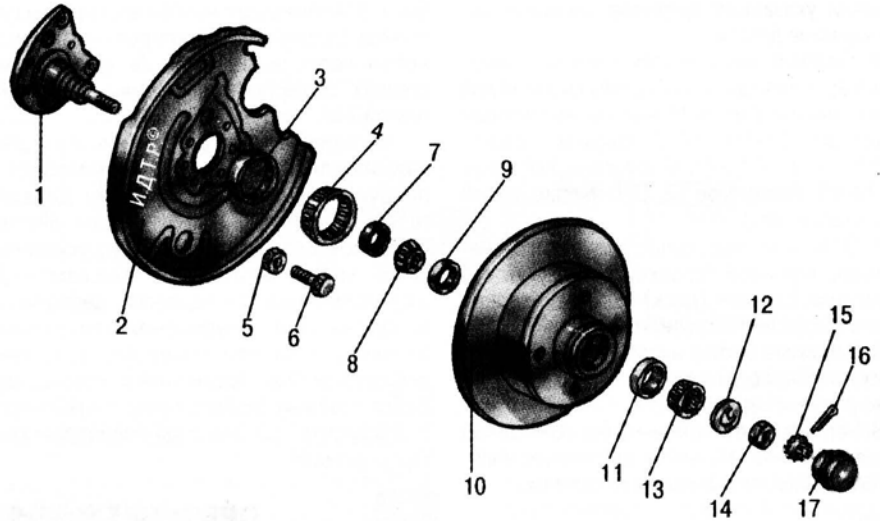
Тормозной диск (ступица) и его детали: 1 – цапфа; 2 – тормозной шит; 3 – кольцо; 4 – венец датчика АБС; 5 – шайба; 6 – болт; 7 – сальник; 8 – внутреннее кольцо внутреннего подшипника; 9 – наружное кольцо внутреннего подшипника; 10 – диск (ступица); 11 – наружное кольцо наружного подшипника; 12 – упорная шайба; 13 – внутреннее кольцо наружного подшипника; 14 – гайка ступицы; 15 – корончатая стопорная шайба; 16 – шплинт; 17 – защитный колпак
